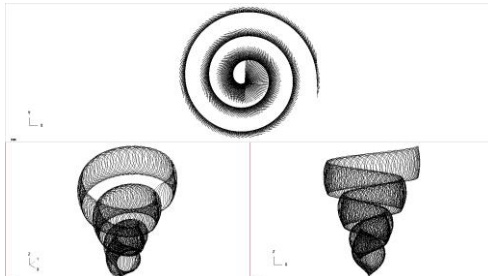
Кинематична схема на фрезование на конусна повърхнина, когато заготовката и инструментът са с пресичащи се оси на стругов център.
